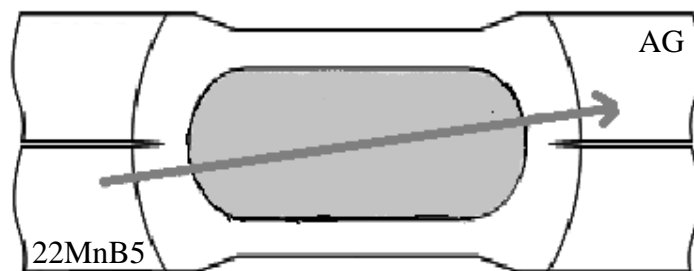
Sentido das medidas de microdureza para juntas soldadas por ponto de solda.
